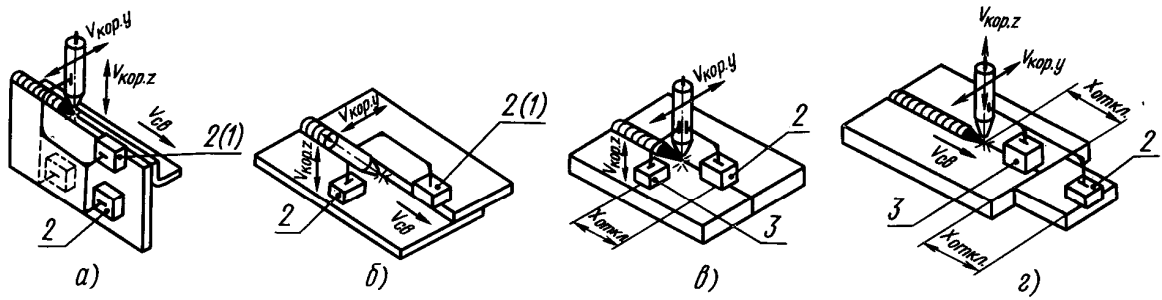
Размещение датчиков при сварке различных соединений
